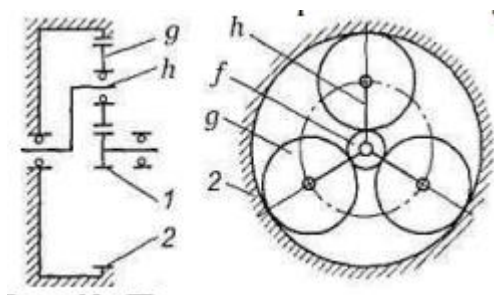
Планетарная передача: 1- колесо с наружными зубьями; 2 колесо с внутренними зубьями; g – планетарные колеса; h – водило; f – солнечная шестерня
